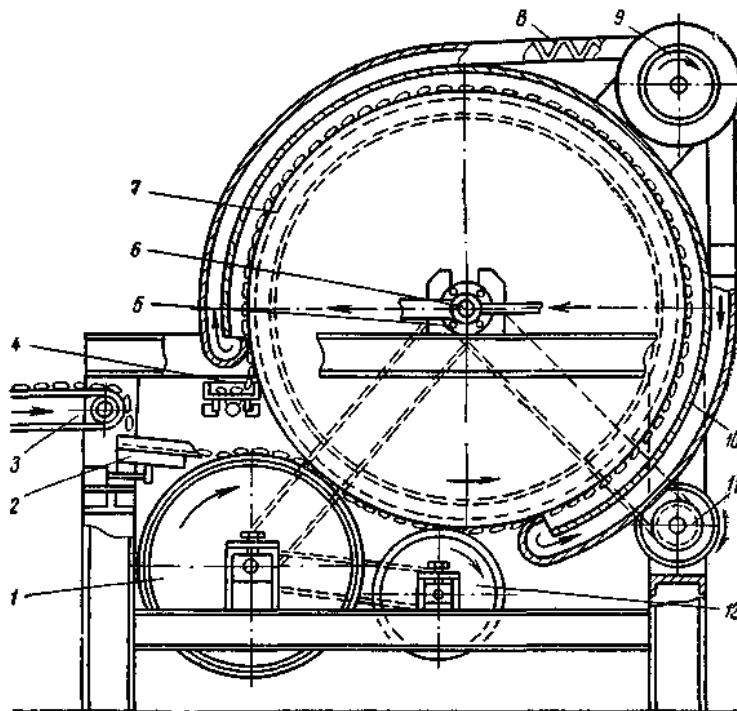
Морозильний апарат барабанного типу для заморожування вологих продуктів неправильної форми: 1 – живильний барабан; 2, 4 – вібротоки; 3 – вхідний конвеєр; 5 – підшипники; 6 – вал; 7 – заморожувальний барабан; 8 – повітроохолоджувач; 9 – вентилятор; 10 – кожух; 11 – електродвигун; 12 – прижимний барабан
